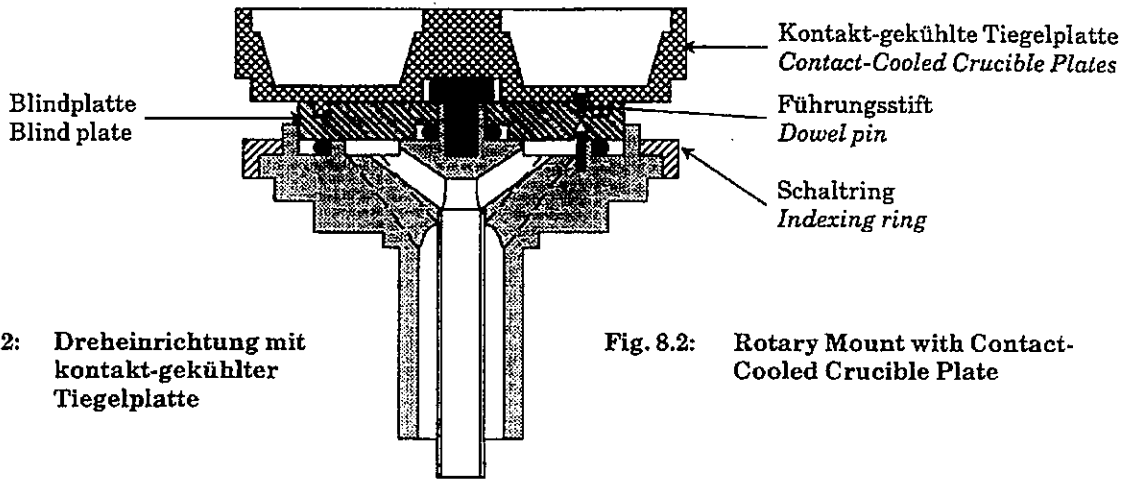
Dreheinrichtung mit kontakt-gekühlter Tiegelplatte
